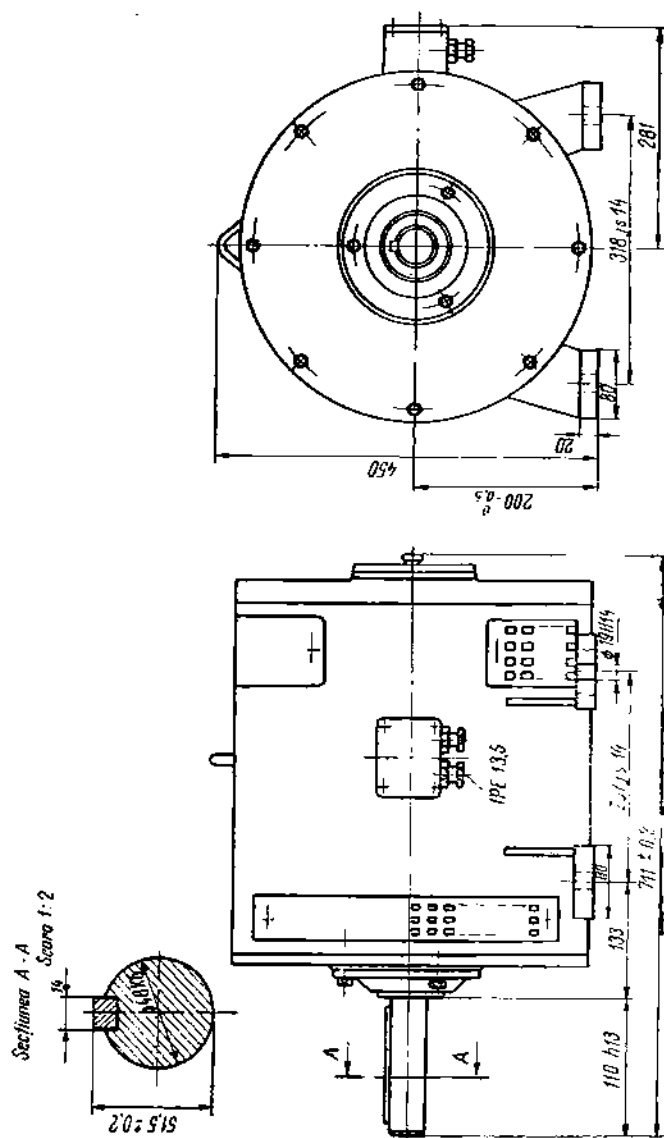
Motor tip Ce 200 M — 10 kW. Dimensiuni de montaj.
